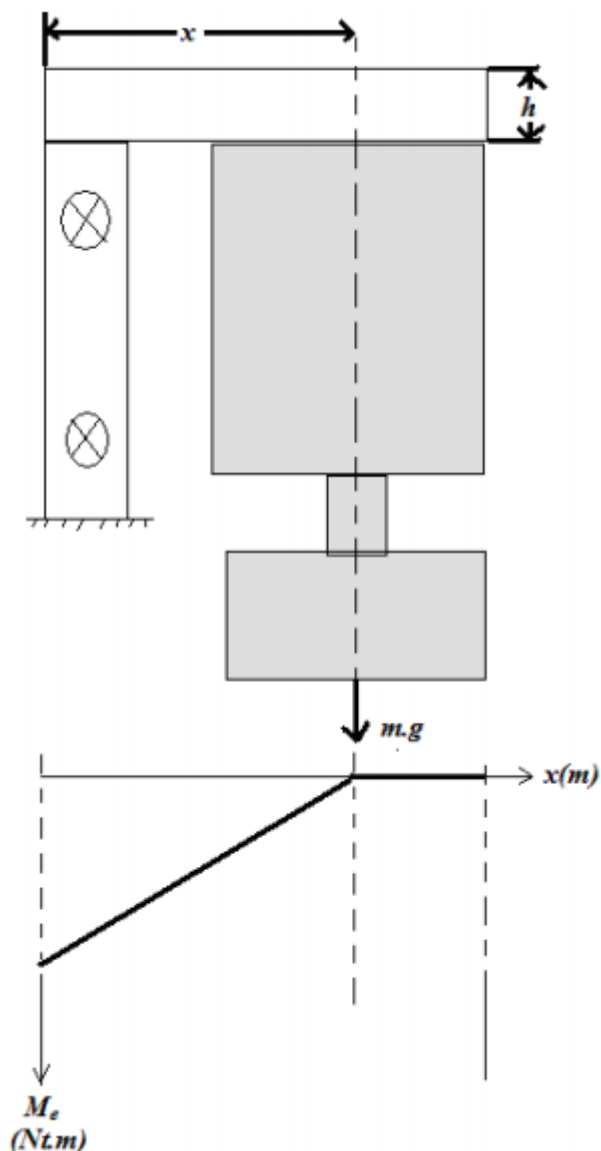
Модель згинання елементів, що утримують захват
